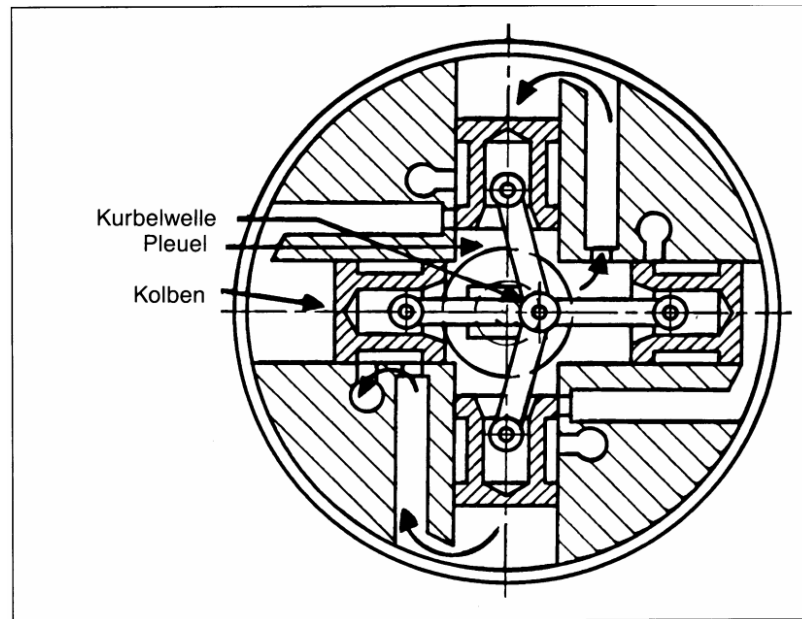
Schnittbild Kolbenzähler der Serie Milliflow®
